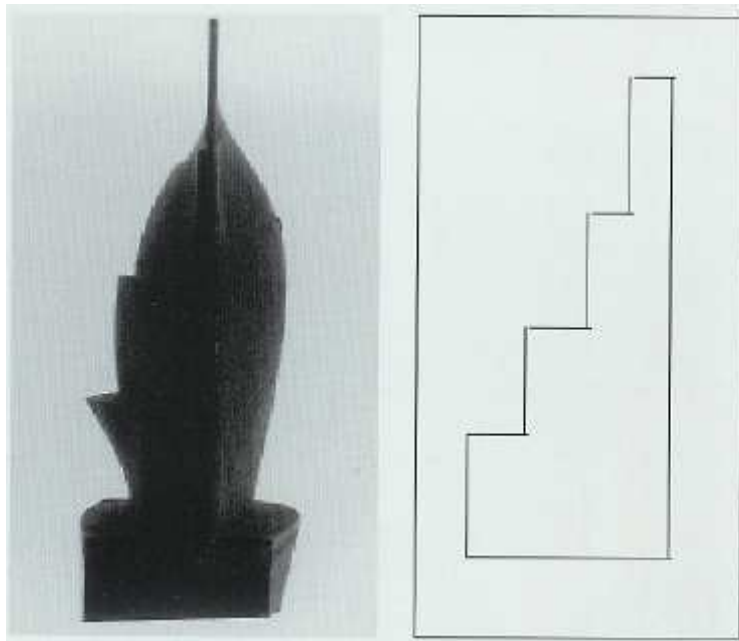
Oddělení jednotlivých vrstev skořepiny [16]
